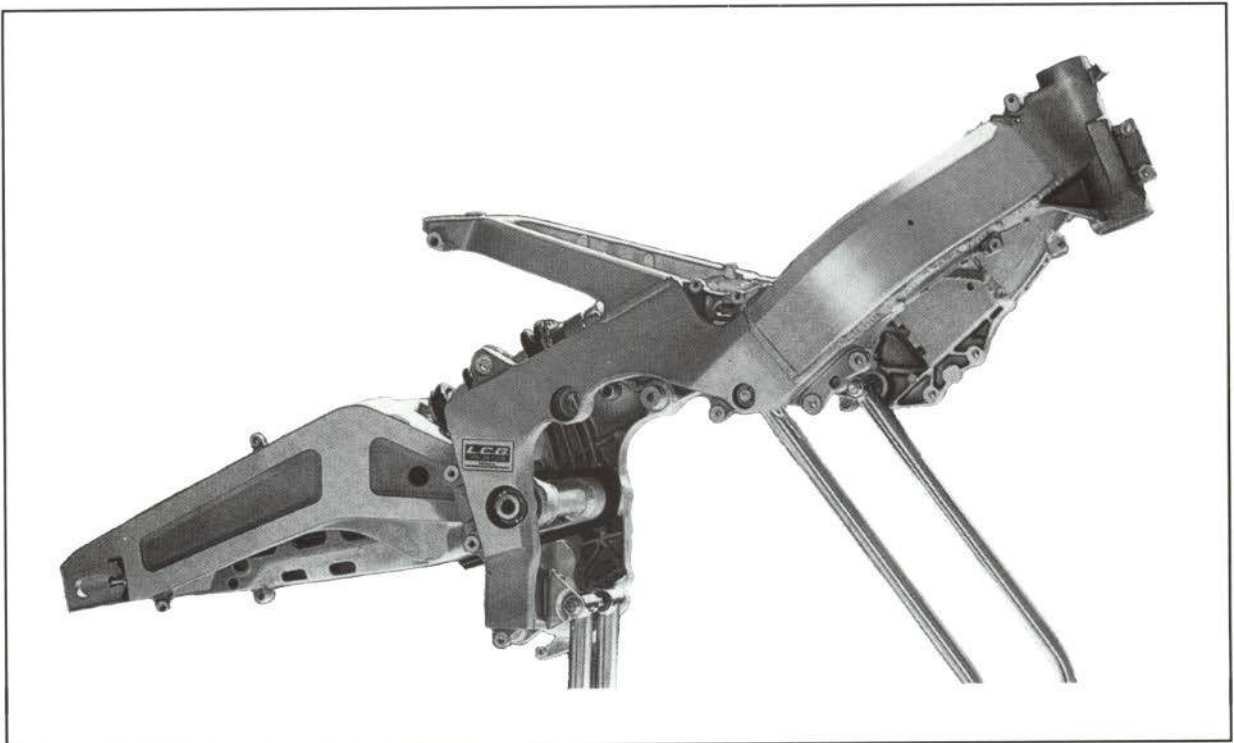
Chasis doblecuna. Viga perimetral abierta. Honda CBR 400 RR.
